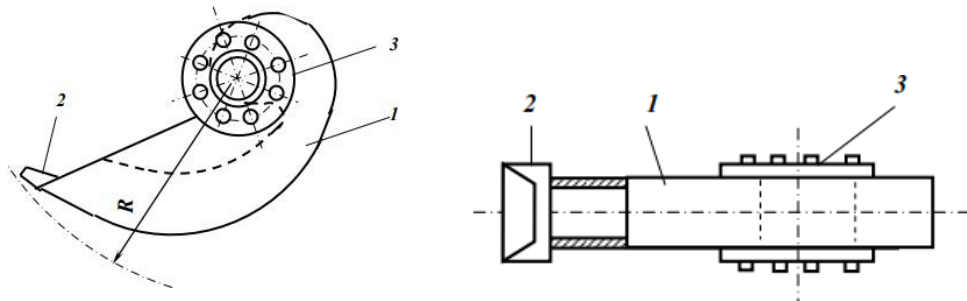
Равликовий живильник. 1 – корпус; 2 – козирок ; 3 – фланець.
